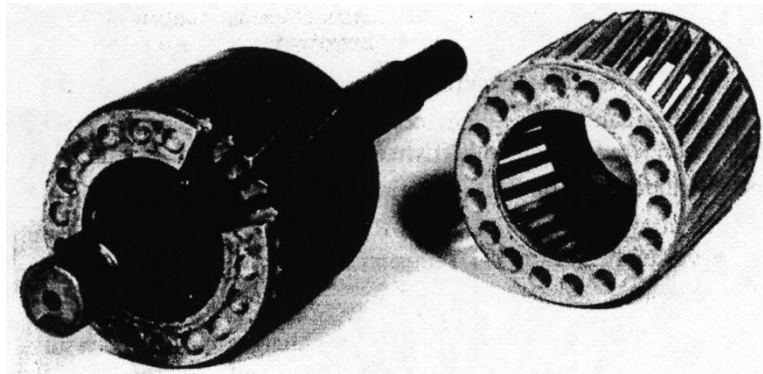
Kurzschlussläufer (links) mit Aluminium Käfig (rechts) für 4 kW-Motor.
